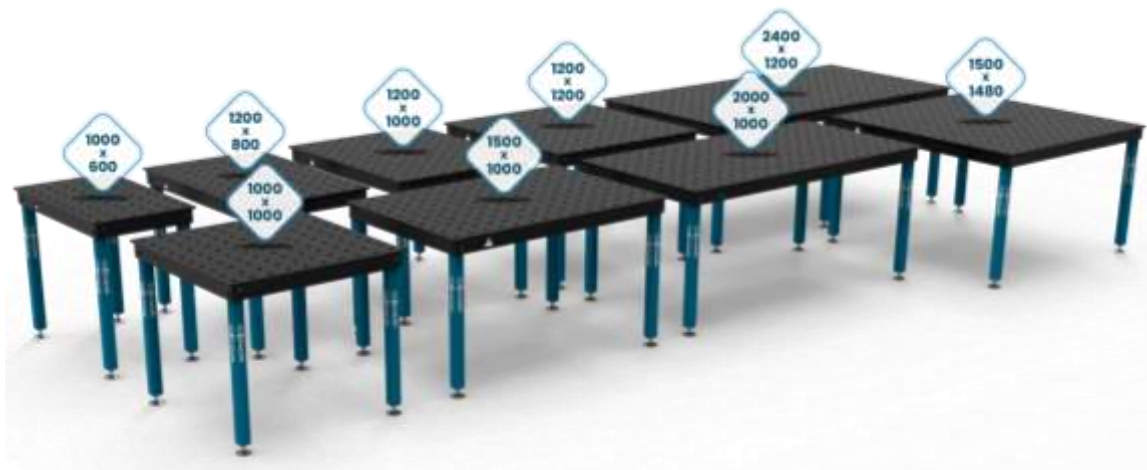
Типові розміри стільниць зварювальних столів
